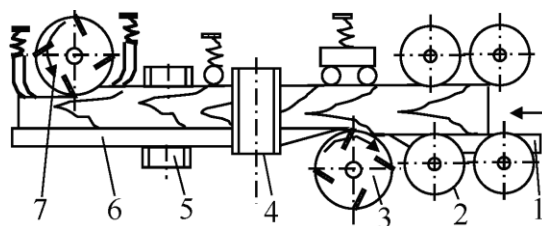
Схеми чотирибічного поздовжньо-фрезерного верстата
